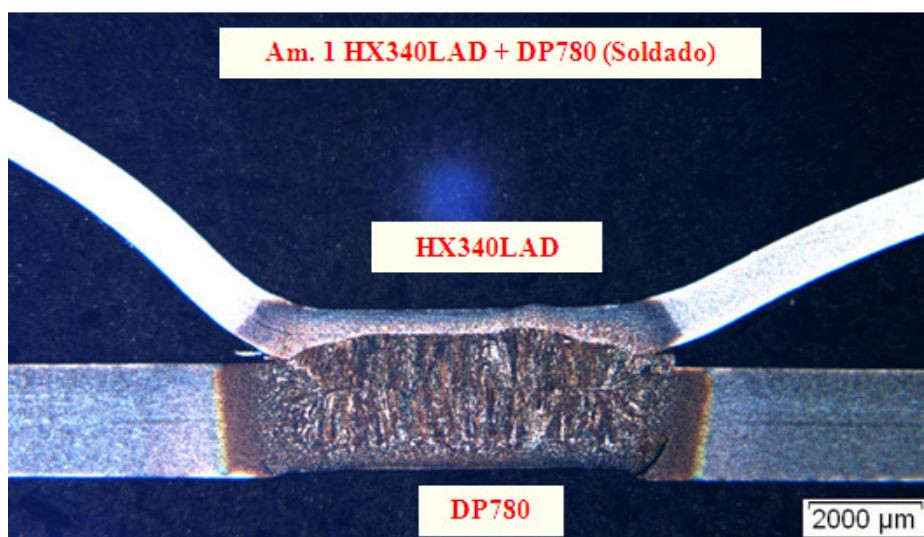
União soldada HX340LAD – DP780 (20X).
